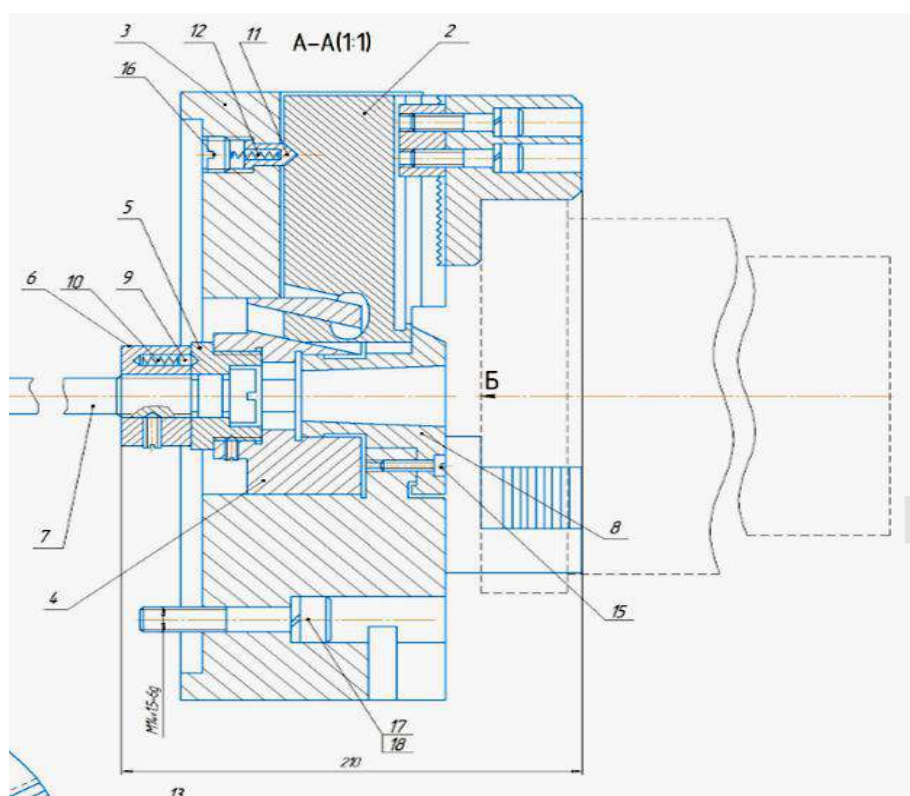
Схема приспособления патрон пневматический трехкулачковый
